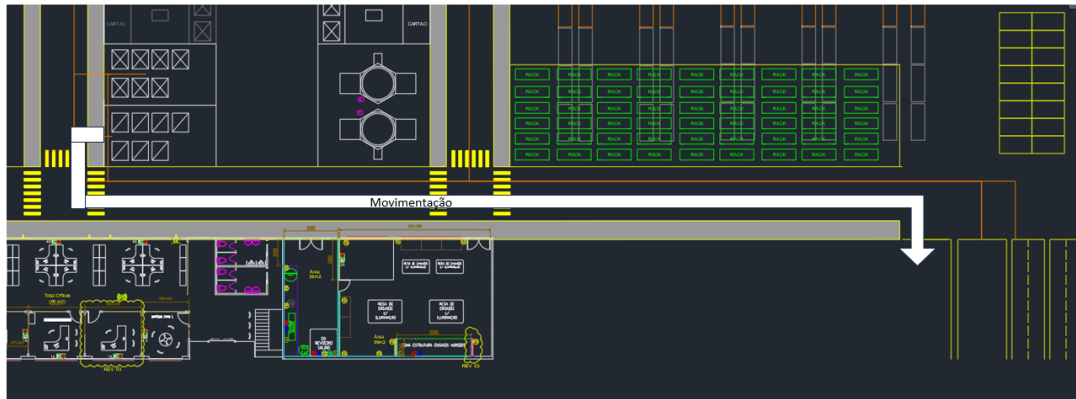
Movimentação entre os setores de Montagem de Cabines/Montagem de Acessórios e Expedição.
